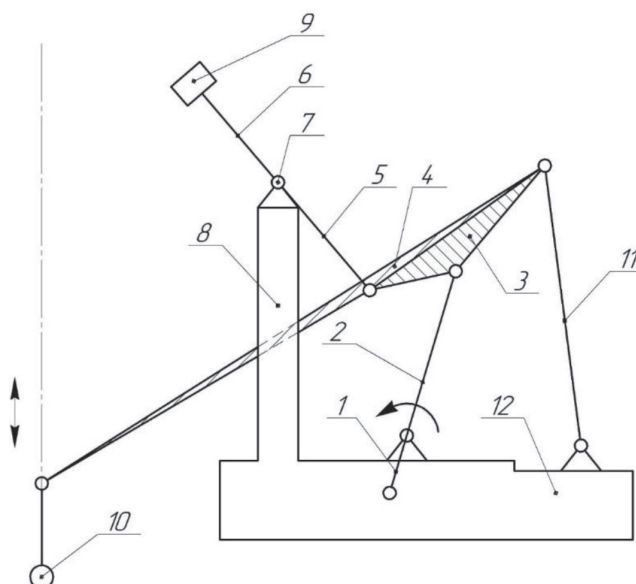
Кинематическая схема механизма привода штанговых насосных установок в нижнем положении
